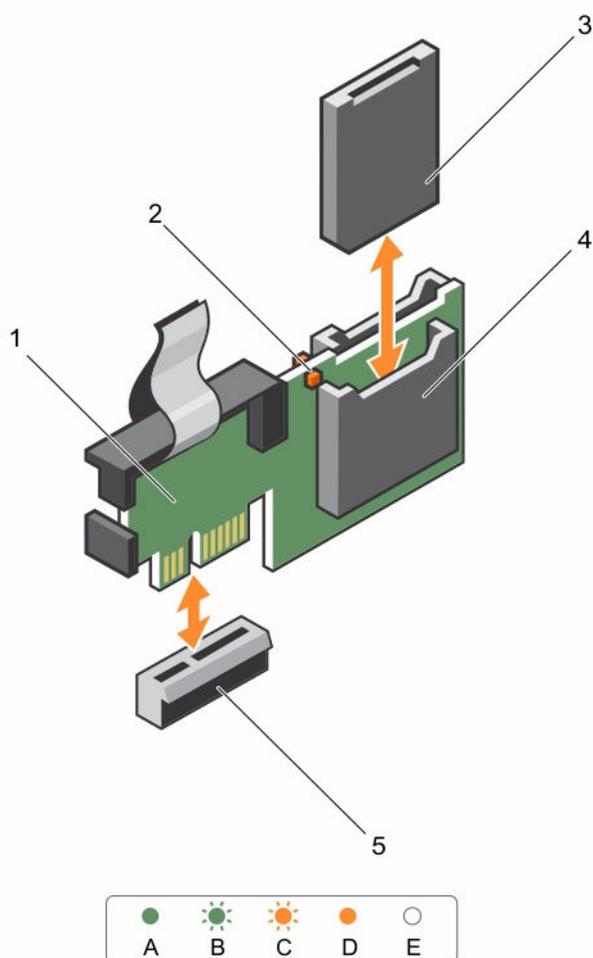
Remover e instalar o IDSDM (Internal Dual SD Module)
